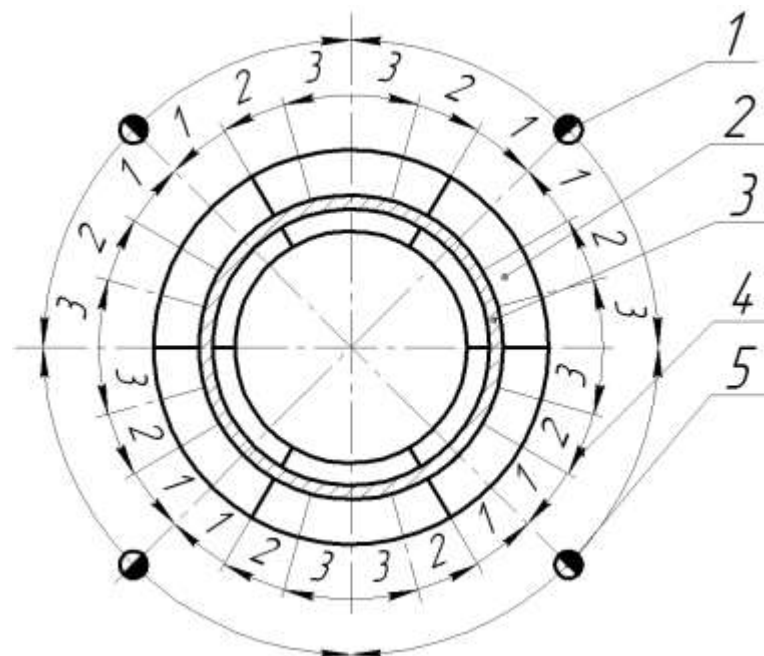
Пример схемы сварки участками обечайки с опорным кольцом:
